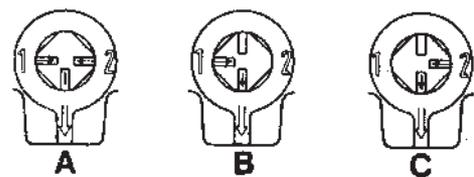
Positions du robinet 3 voies, filtre à carburant réversible
